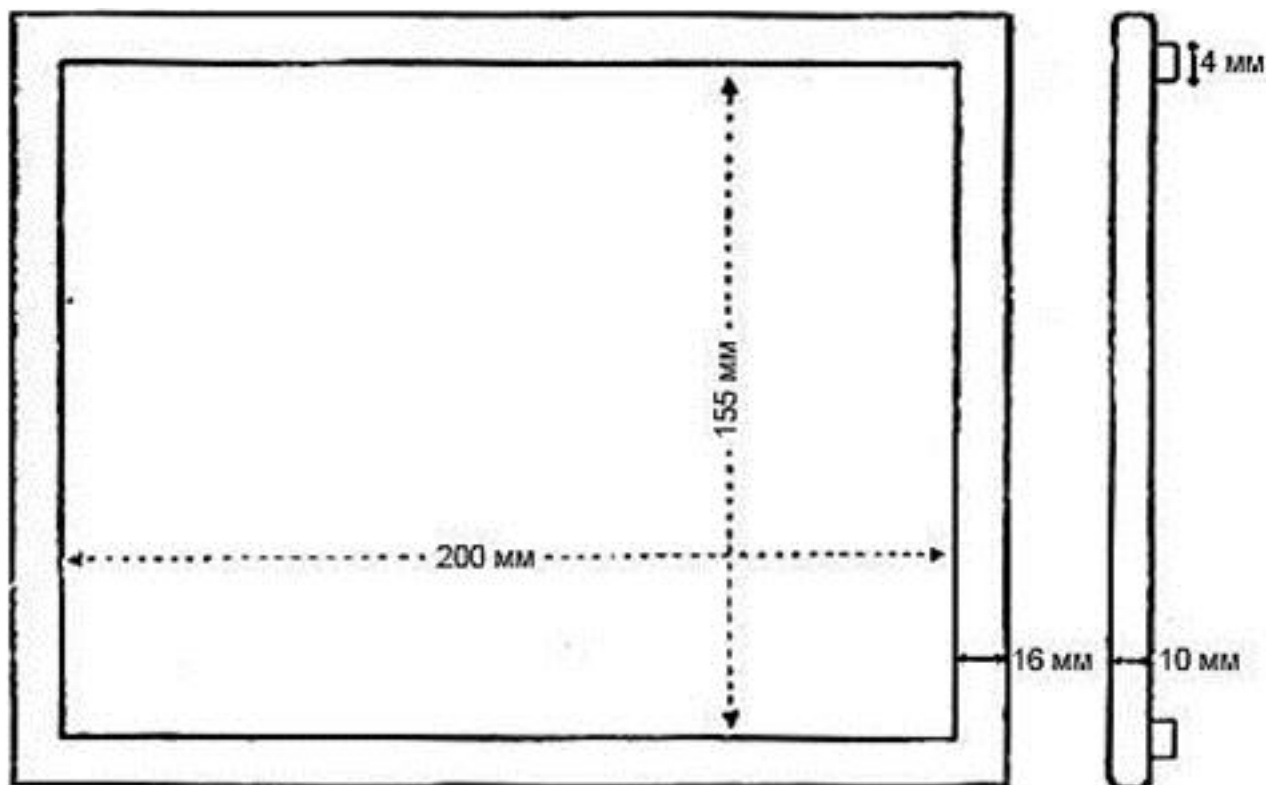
Размерный чертеж рамочки для проявления пленки.
